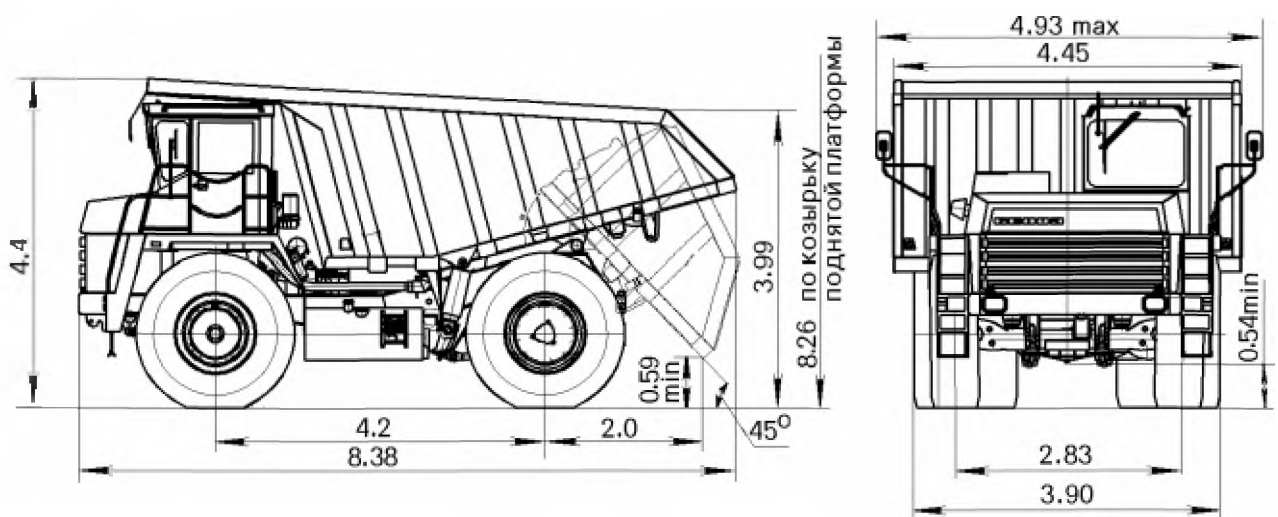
Самосвал-углевоз БелАЗ-75479. Габаритные размеры
